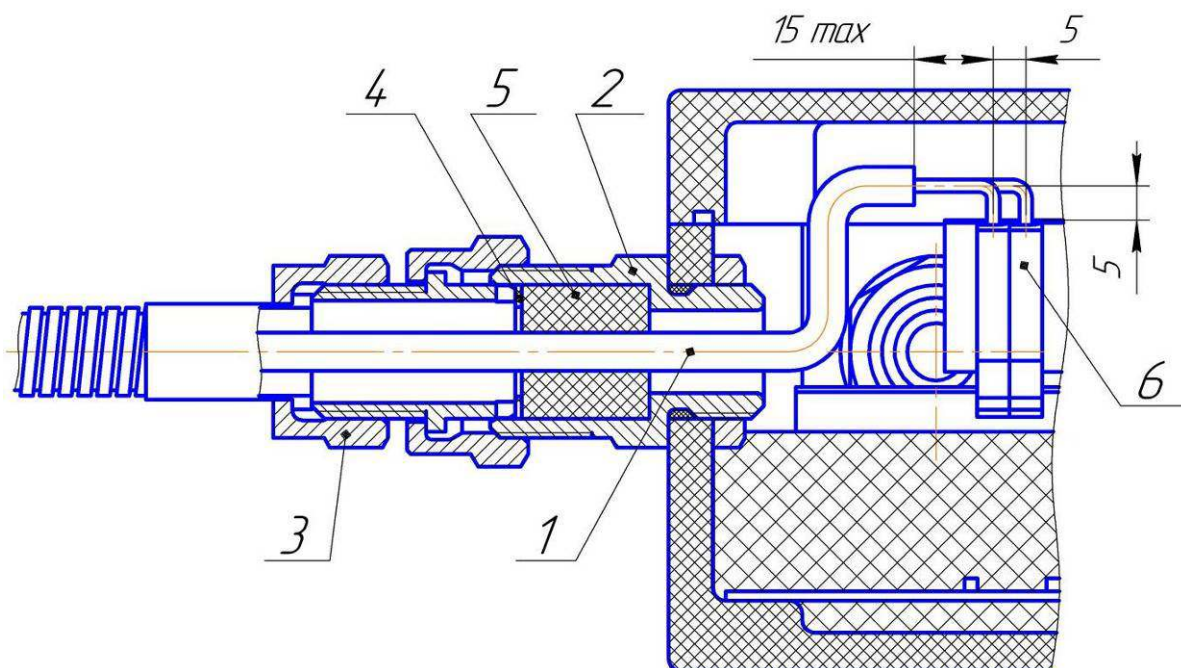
БУШ. Устройство, габаритные и присоединительные размеры
